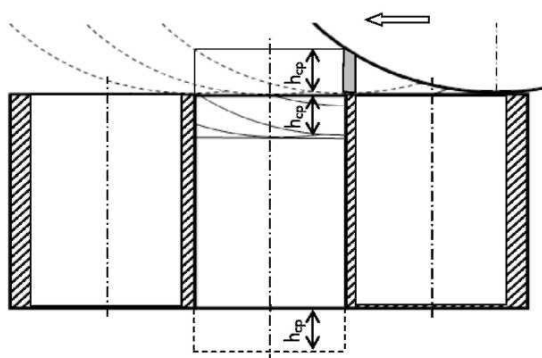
Схема обкатывания матрицы прессовочным роликом
